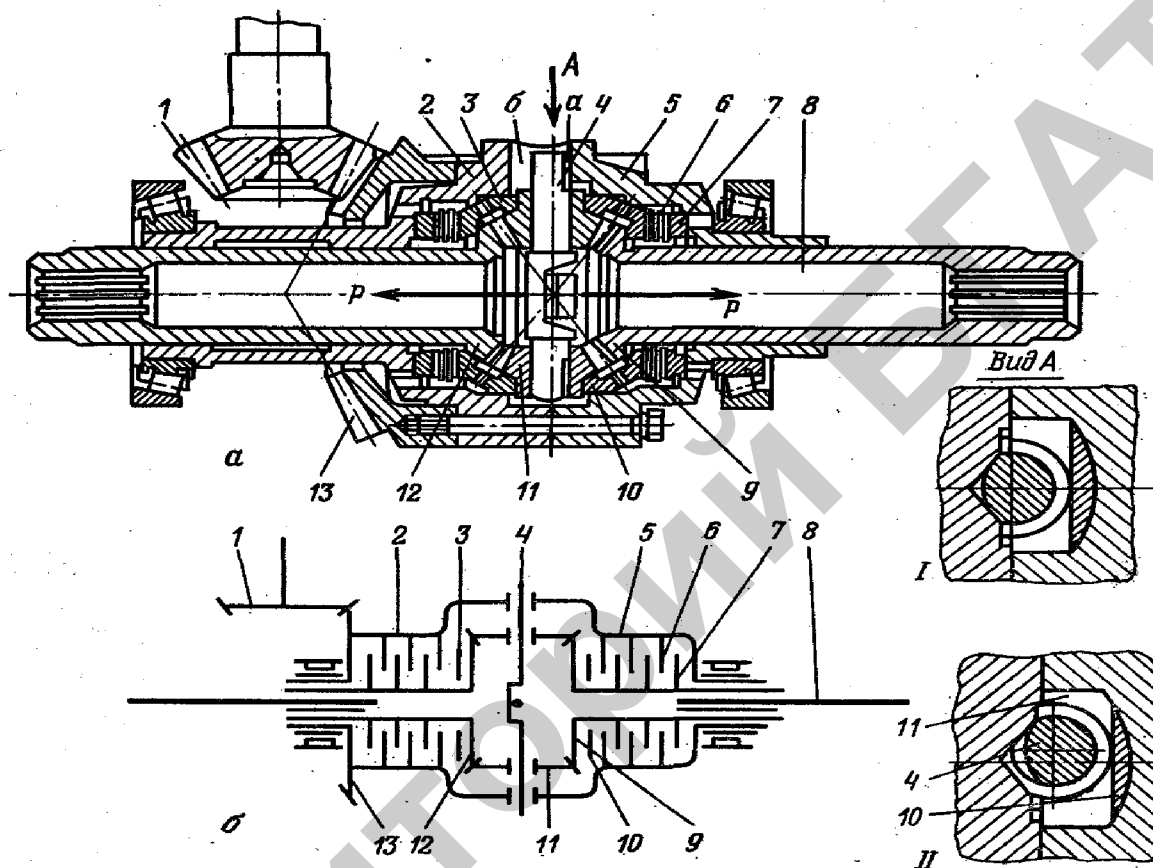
Самоблокирующийся дифференциал с механизмом повышенного трения: а – устройство; б – кинематическая схема; 1 и 13 – шестерни главной передачи; 2 и 5 – половины корпуса; 3 и 10 – нажимные чашки; 4 – оси сателлитов; 6 – ведущий диск; 7 – ведомый диск; 8 – полуось; 9 и 12 – конические шестерни; // – сателлит; I и II – положения сателлитов
